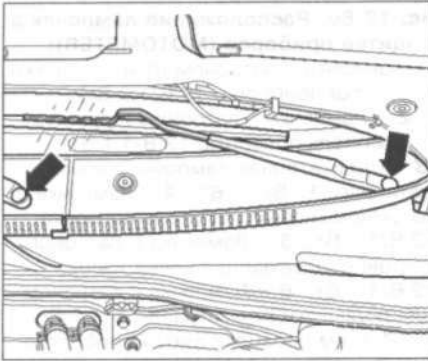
Снимите крышки (стрелки) с помощью отвертки.
